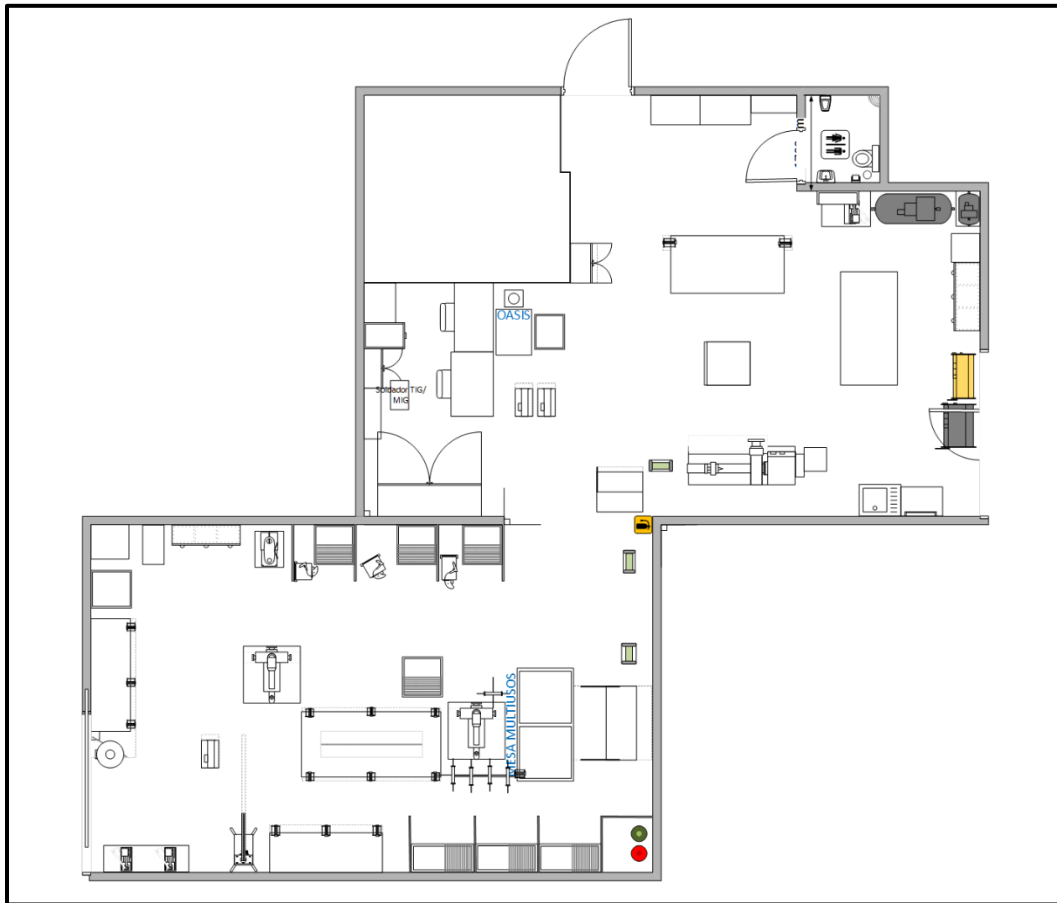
Distribución en planta del taller de Ingeniería Industrial
